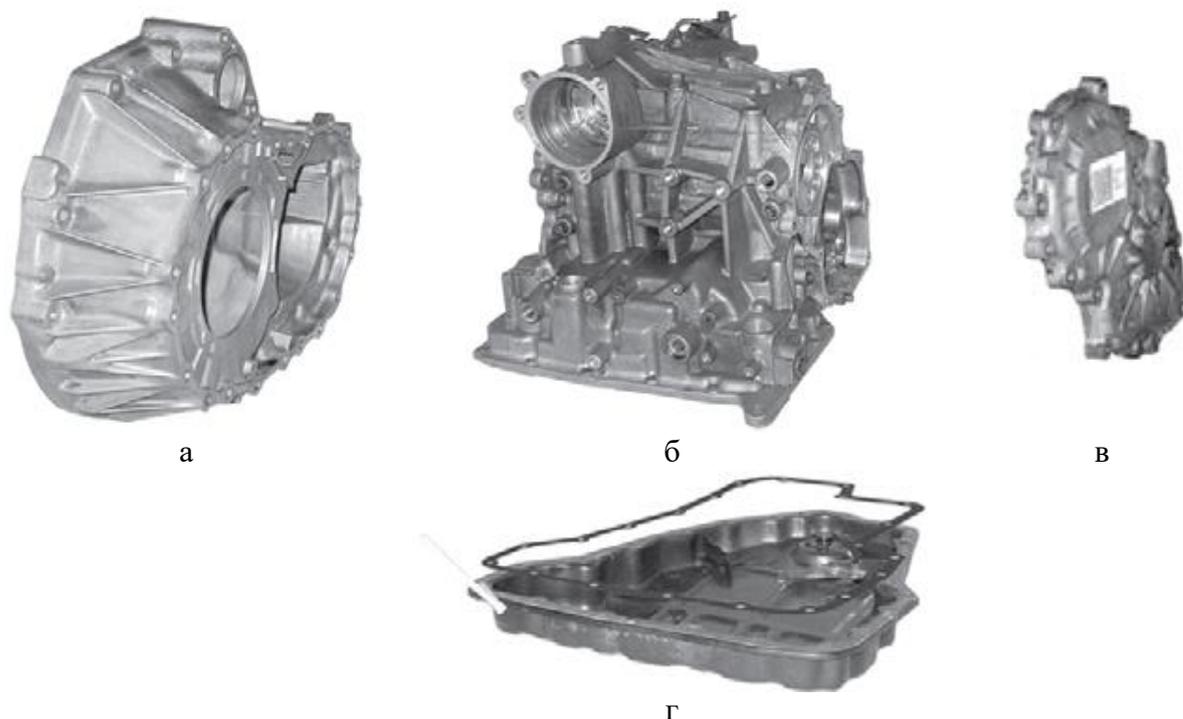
Корпусные детали ГМП автомобиля Lada Granta: а) кожух гидротрансформатора; б) картер ГМП; в) задняя крышка; г) крышка гидроблока.
